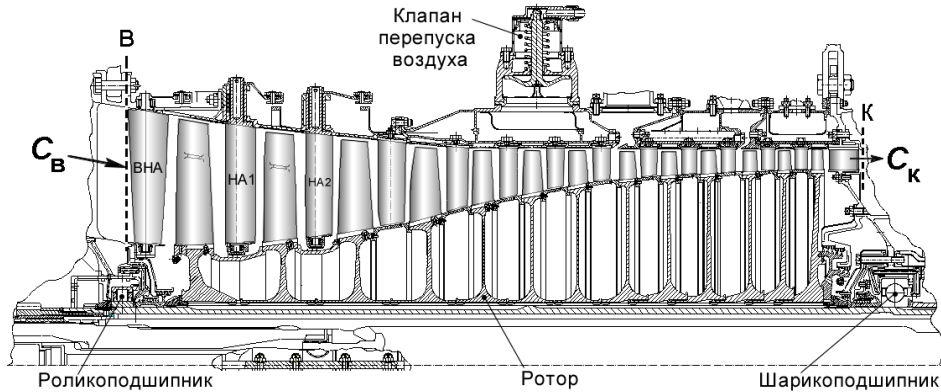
Схема компрессора высокого давления двигателя ПС-90А
